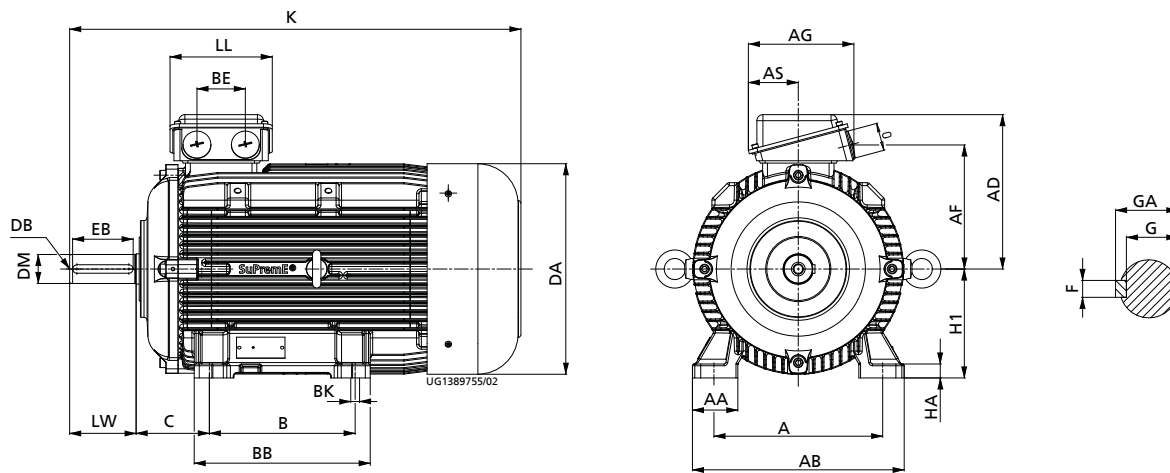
Исполнение со стандартной крышкой подшипника (B3,...)
